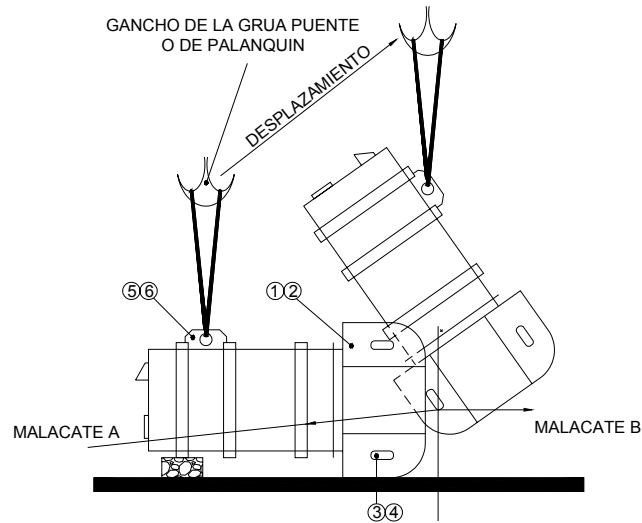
Levantamiento del transformador con grúa puente.
